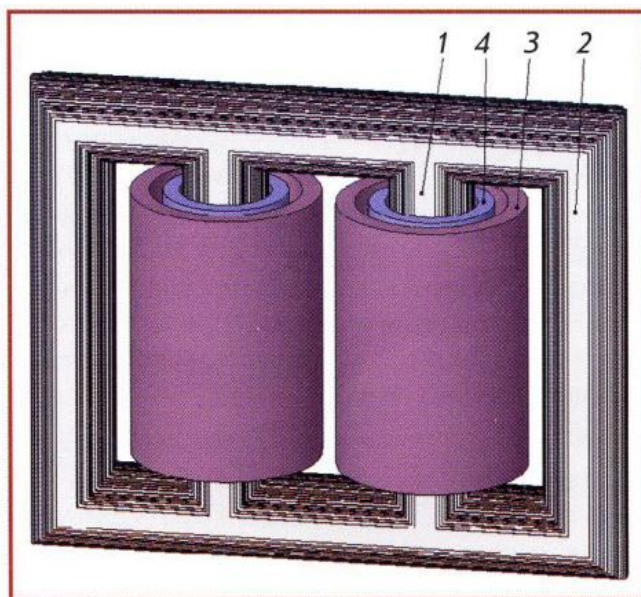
Конструкція фази КШР 110 кВ: 1 – основний (робочий стрижень); 2 – бокове ярмо; 3 – мережева (реакторна) обмотка.
